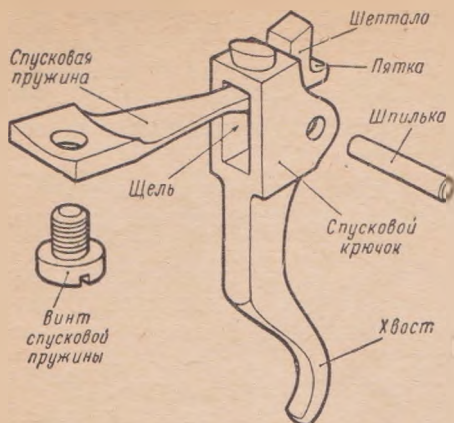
Спусковой механизм армейской винтовки образца 1891/30 гг.
